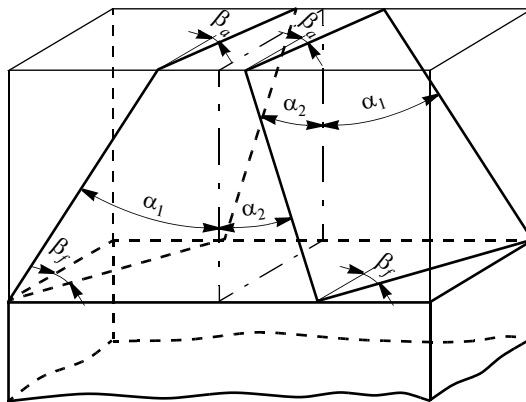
Схема предлагаемой формы режущей части поворотных твердосплавных зубьев-пластин, обеспечивающая при поворотах требуемый профиль (для лезвостроительной фрезы): α_1 и α_2 — профильные углы левой и правой сторон соответственно; β_a и β_f — углы подъема на вершине и впадине
